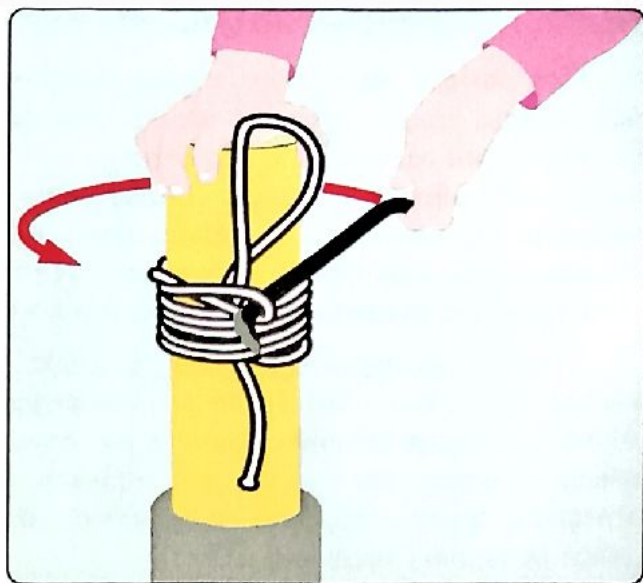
Проворачивание втулки с помощью веревки со свободными концами
